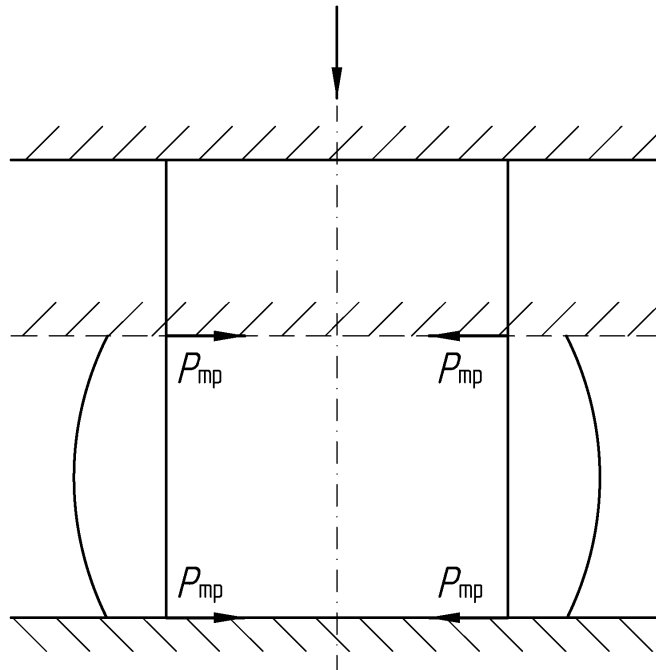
Схема процесса осадки цилиндрической заготовки и направления действующих на контакте сил трения
